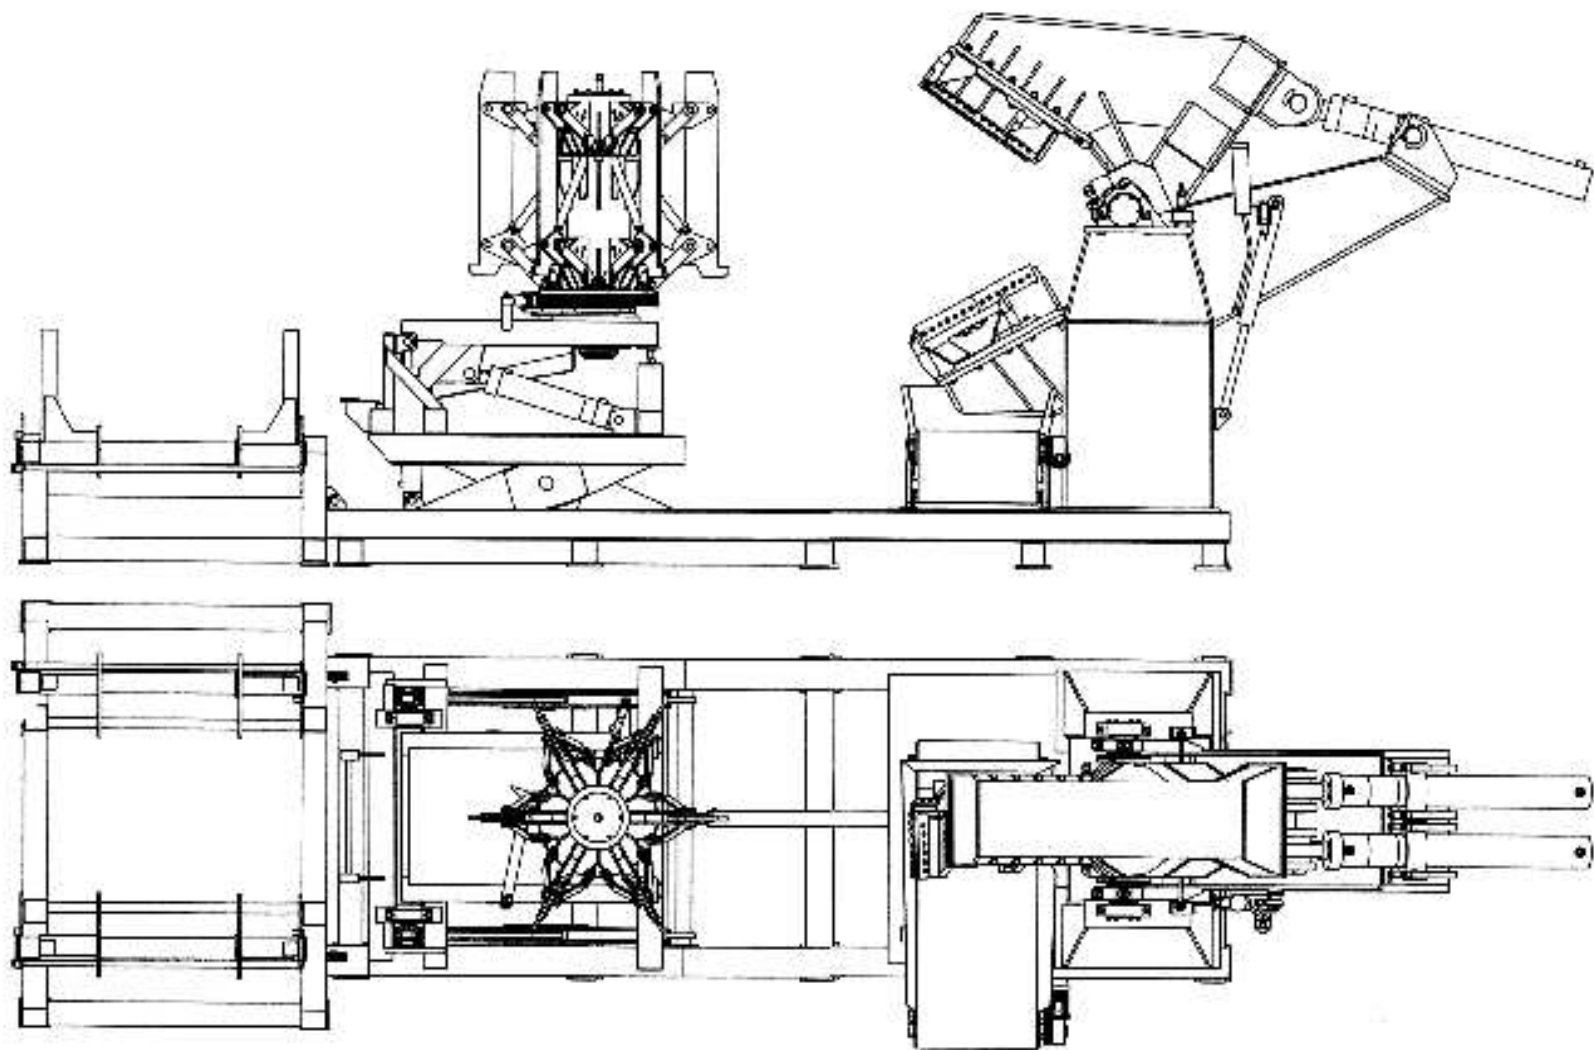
Сборочный чертеж установки «Челюсти»
